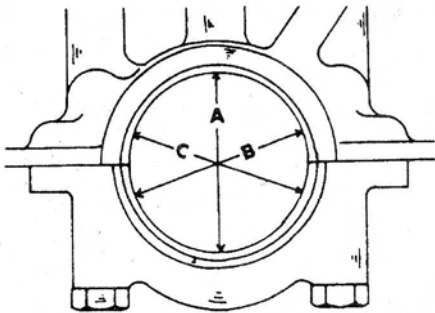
Измерение основного отверстия подшипника коленчатого вала. Измерения проводятся в направлениях А, В и С.
